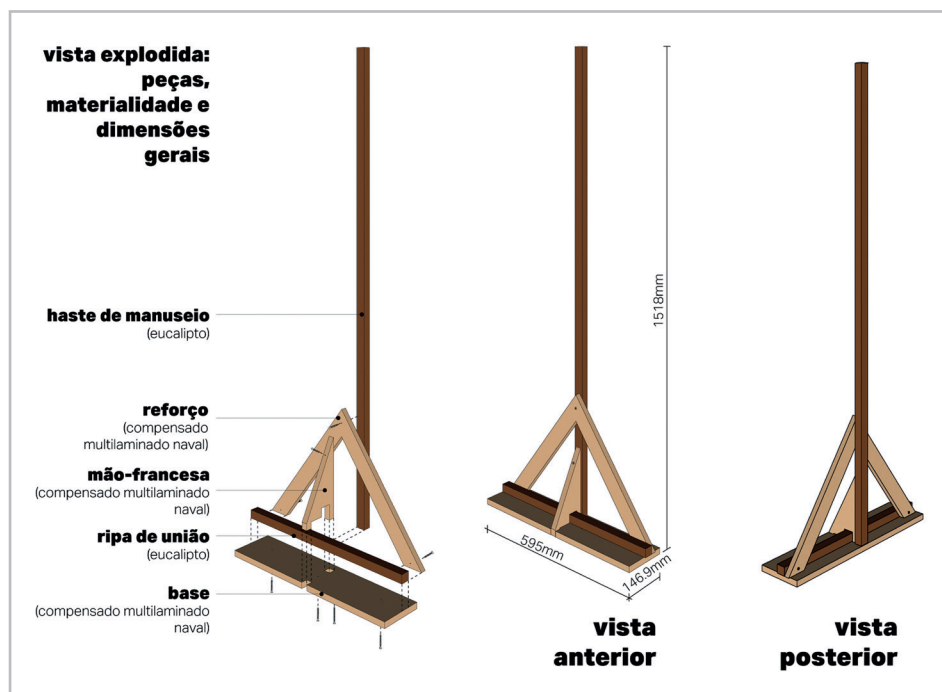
Peças, materialidade, dimensões gerais e vista explodida do modelo final do rodo
